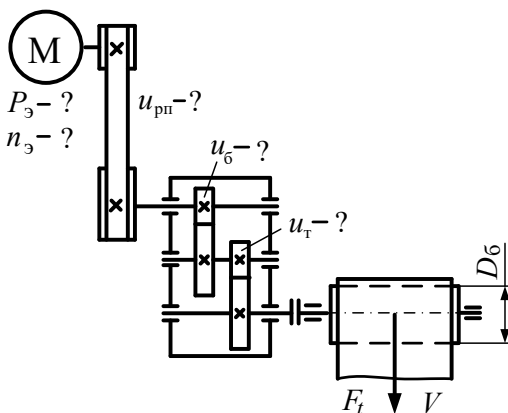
Схема привода ленточного конвейера (Р)
